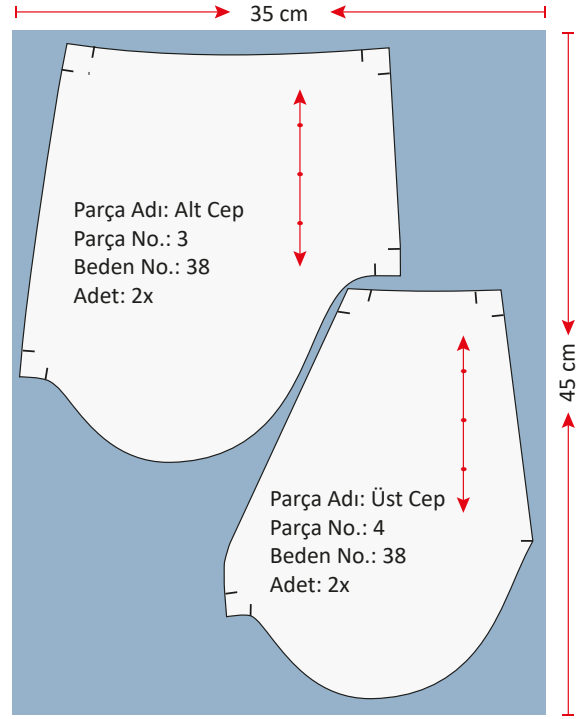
Kadın pantolon kumaş pastal planı çizimi
